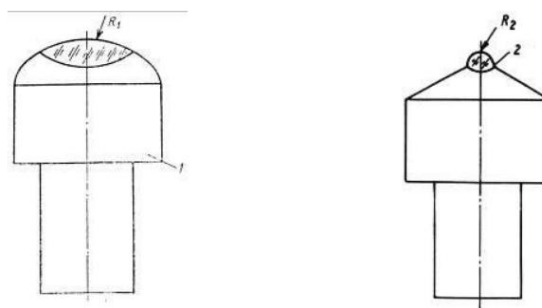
Інструмент з робочою поверхнею, утворена циліндрами різного радіусу.
